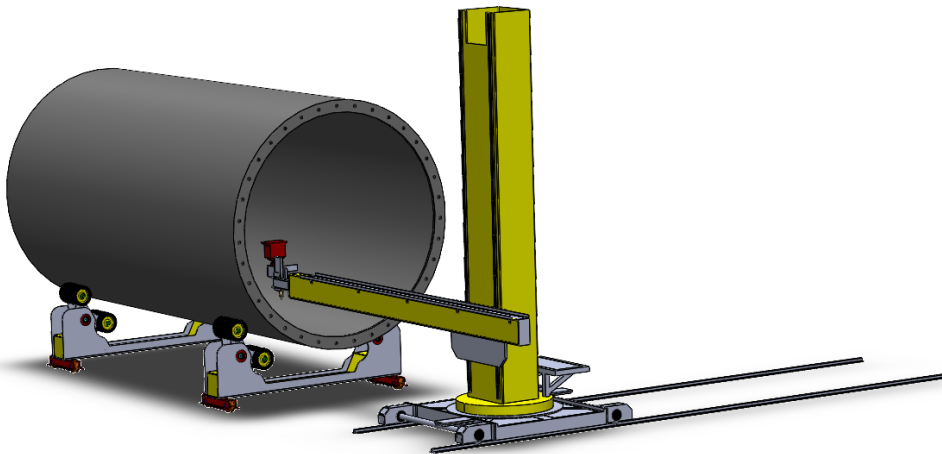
Soldadura longitudinal ou circunferencial internamente
